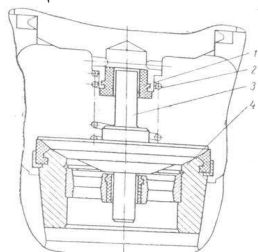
Клапан насоса УНБ-600 в сборе: 1 - втулка; 2 – пружина; 3 – тарелка клапана; 4 – седло в сборе
